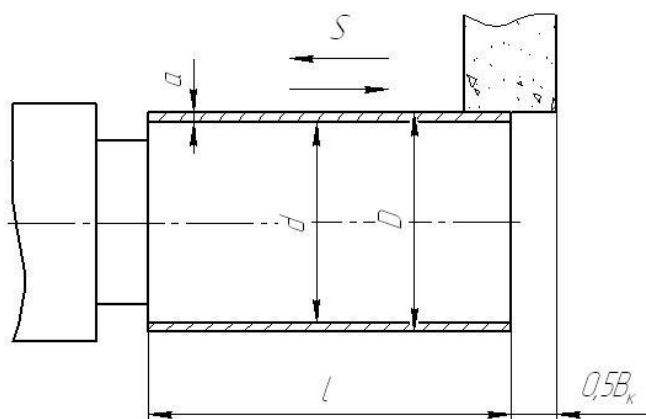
Наружное круглое шлифование методом продольной подачи
